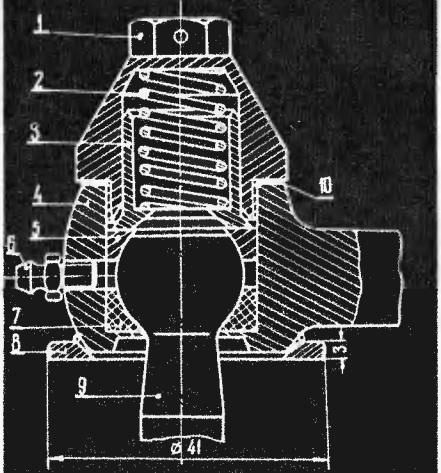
Детали нового шарнира поперечной и боковой рулевых тяг: 1 — заглушка; 2 — пружина; 3 — нажимной поршень; а — отверстие для стопорной проволоки.
